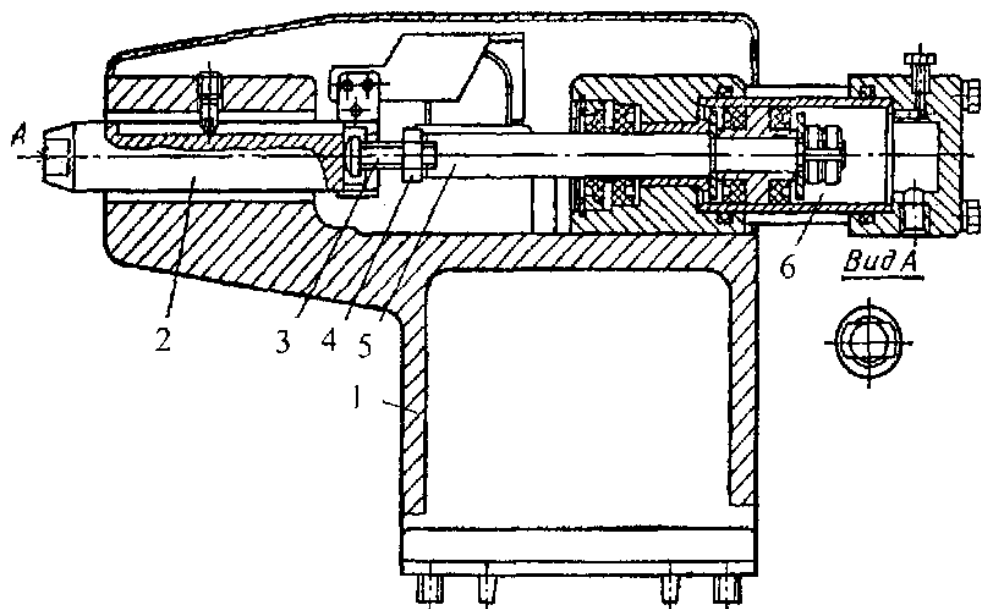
Схема центруючого пристрою: 1 – стояк; 2 – орієнтач; 3 – болт; 4 – гайка; 5 – шток; 6 - гідроциліндр
